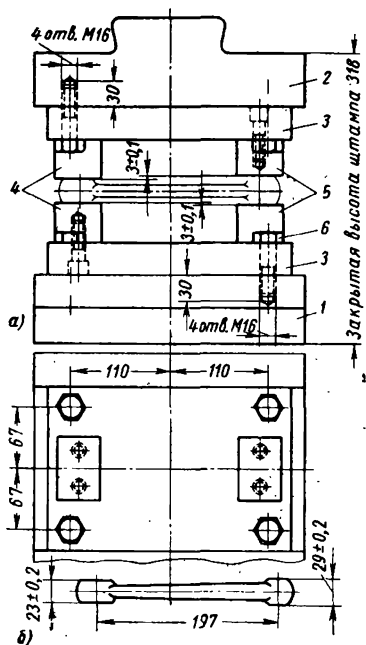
Штамп для плоскостной калибровки рычага: а — общий вид; б — поковка
